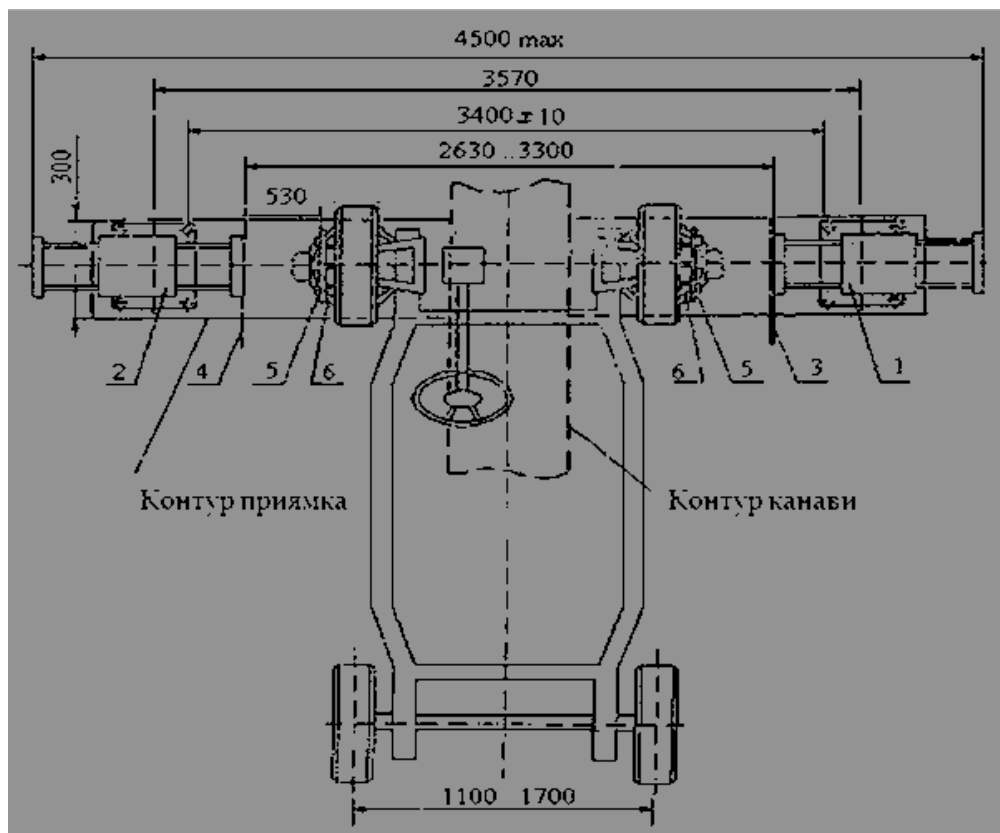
Схема станда: 1 – стійка лазерна права; 2 – стійка лазерна ліва; 3 – шкала права; 4 – шкала ліва; 5 – розпірна консоль; 6 – поворотна платформа
